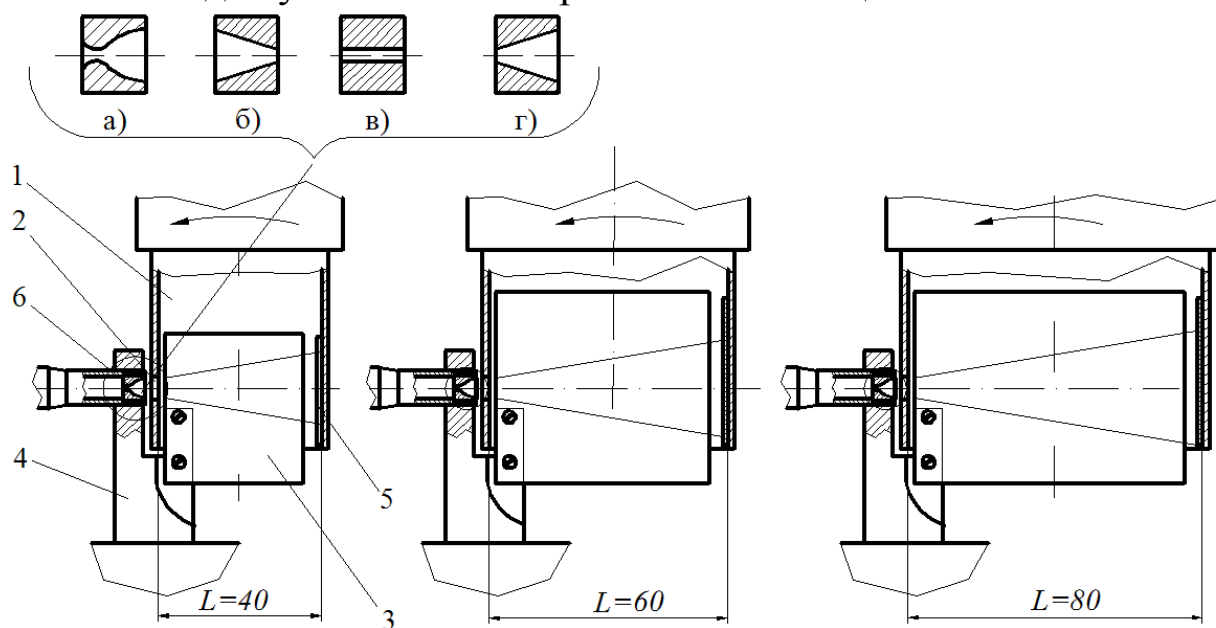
Устройство для определения скорости абразивных зерен в струе сжатого воздуха со сменными соплами: а) – сверхзвуковое сопло Лавала; б) – сужающееся коническое сопло; в) – цилиндрическое сопло; г) - расширяющееся коническое сопло.
